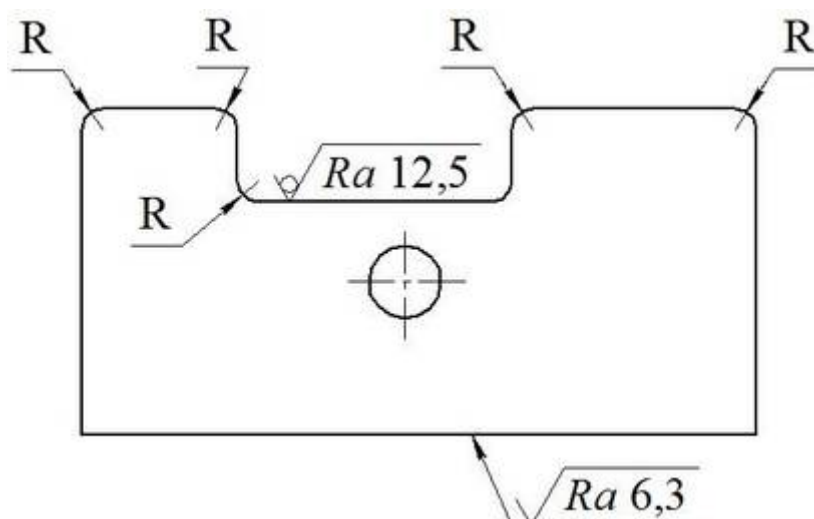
Обозначение одинаковой шероховатости поверхностей, плавно переходящих одна в другую
